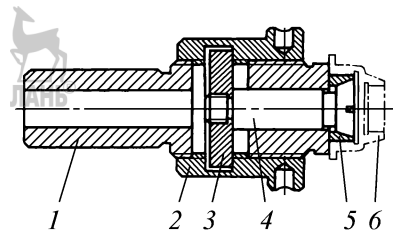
Разжимная оправка с разрезной втулкой:
